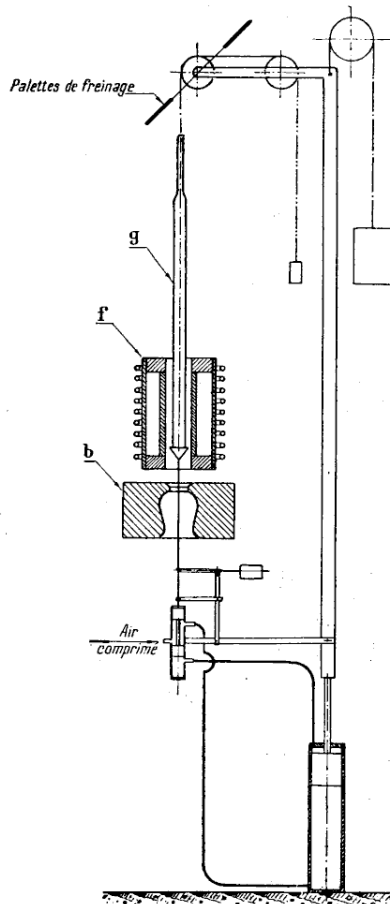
Schéma de la machine automatique à souffler et à mouler.
